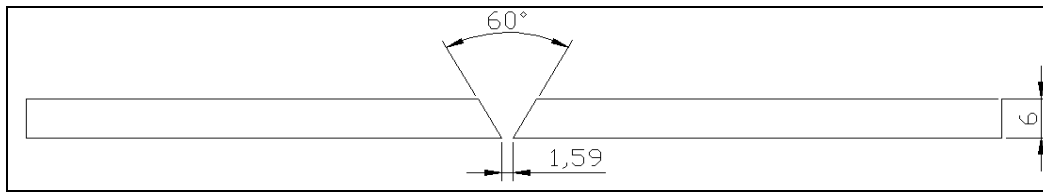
Esquema de diseño de juntas soldadas de acero AISI 1010, dimensiones en mm.
